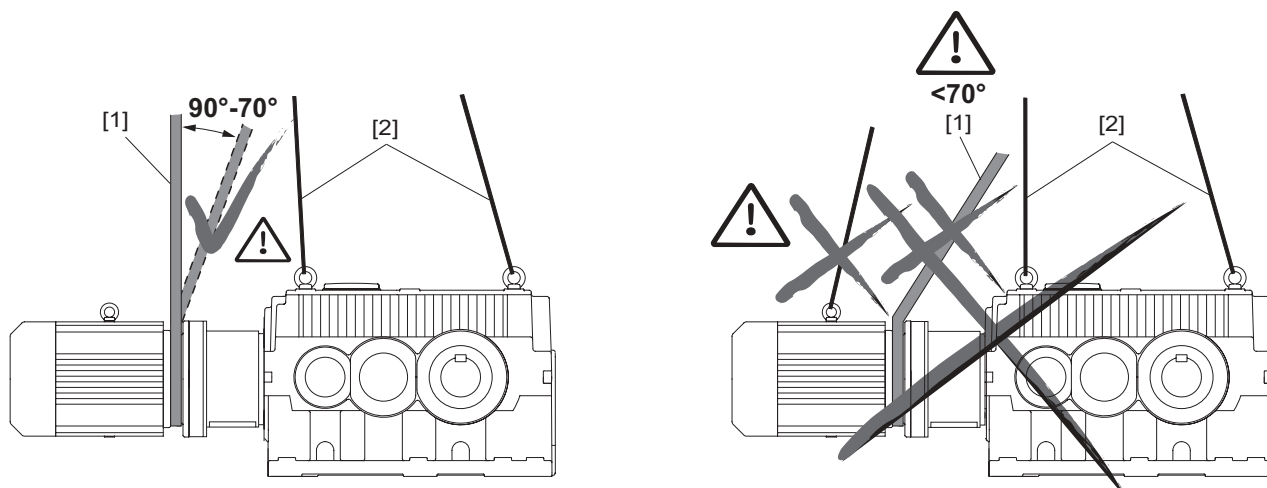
Ne pas utiliser les oeillets de suspension du moteur
